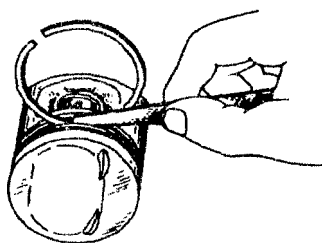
Проверка зазора между поршневыми кольцами и их канавкой
